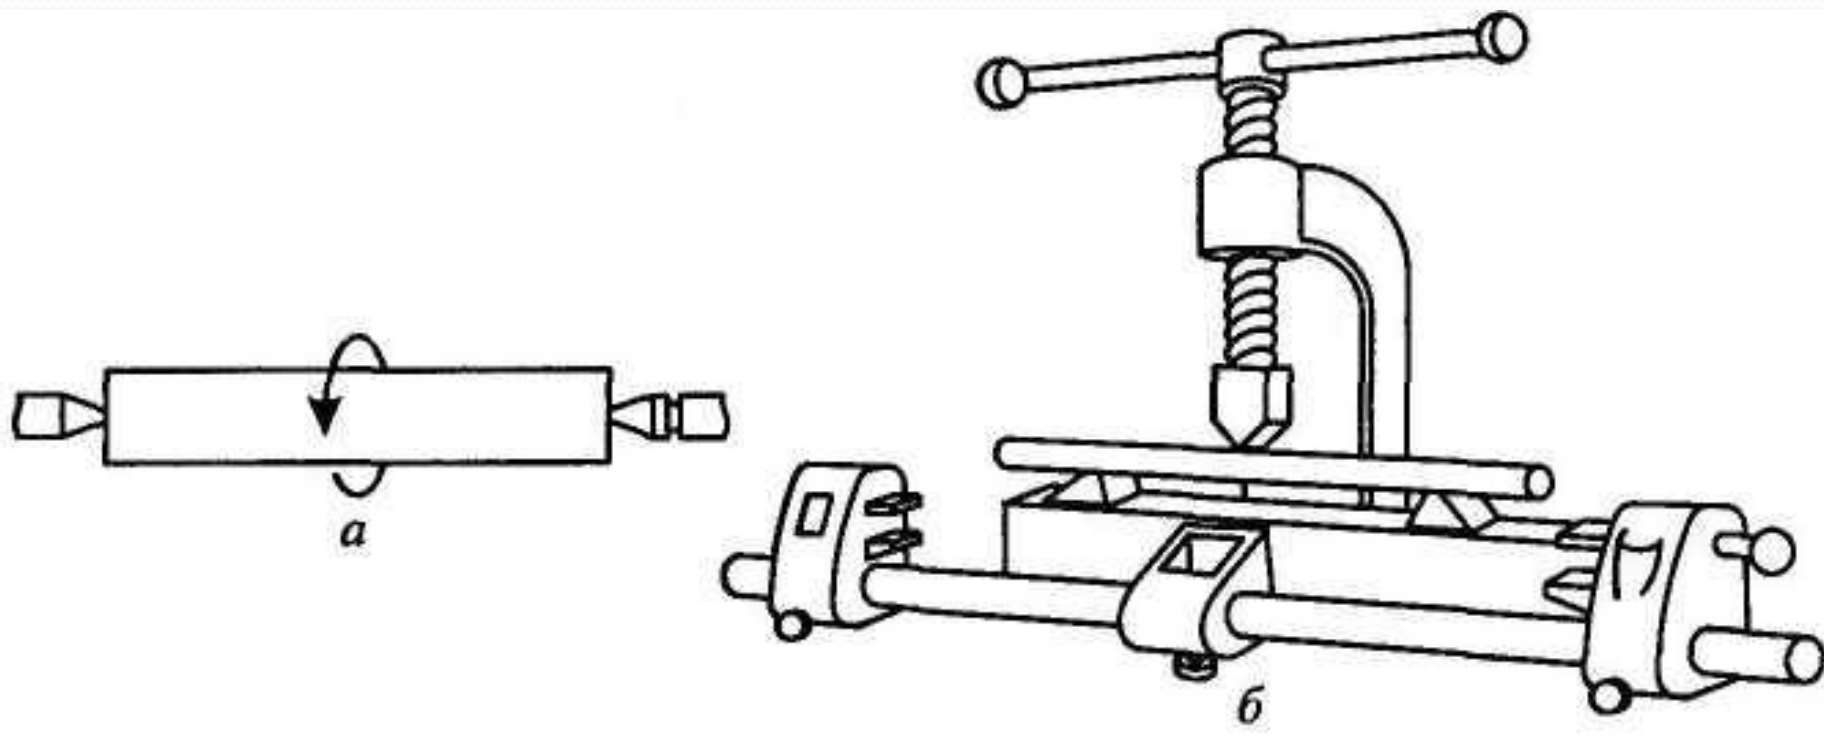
Ручной пресс: а - правка в центрах; б – правка на призмах
